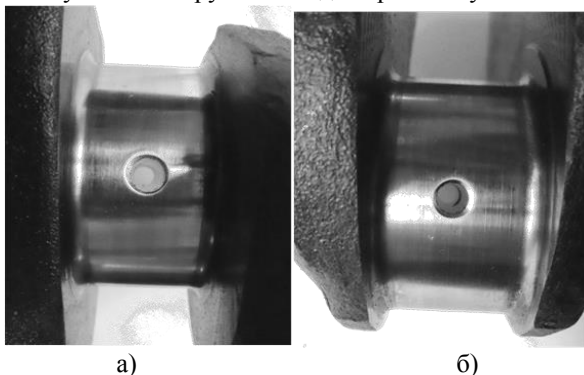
Наружный вид рабочей поверхности шеек коленчатого вала:
